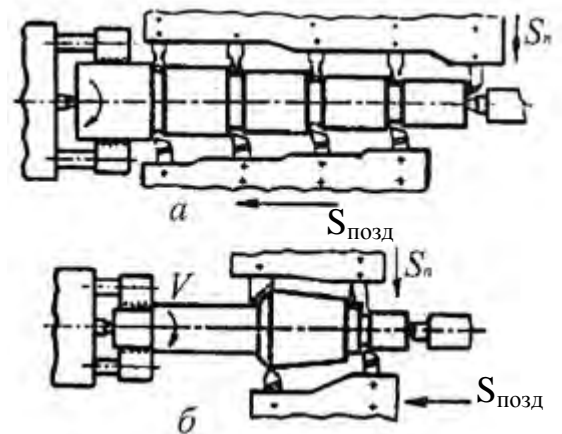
Схеми оброблення заготовок на токарному багаторізцевому напівавтоматі
